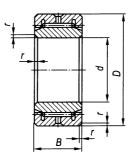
Подшипник роликовый радиальный игольчатый однорядный
